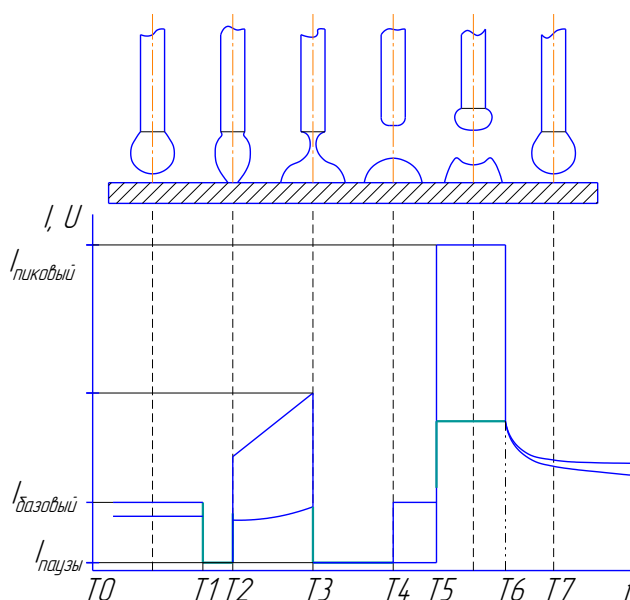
Формы кривых сварочного тока и напряжения при полуавтоматической сварке методом STT
